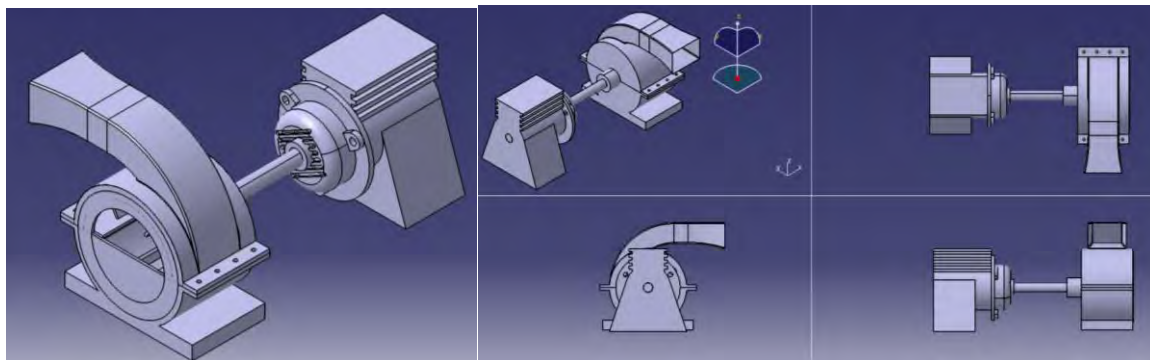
Vistas del ensamble mecánico del soplador y el motor (realizado en Catia V5)
